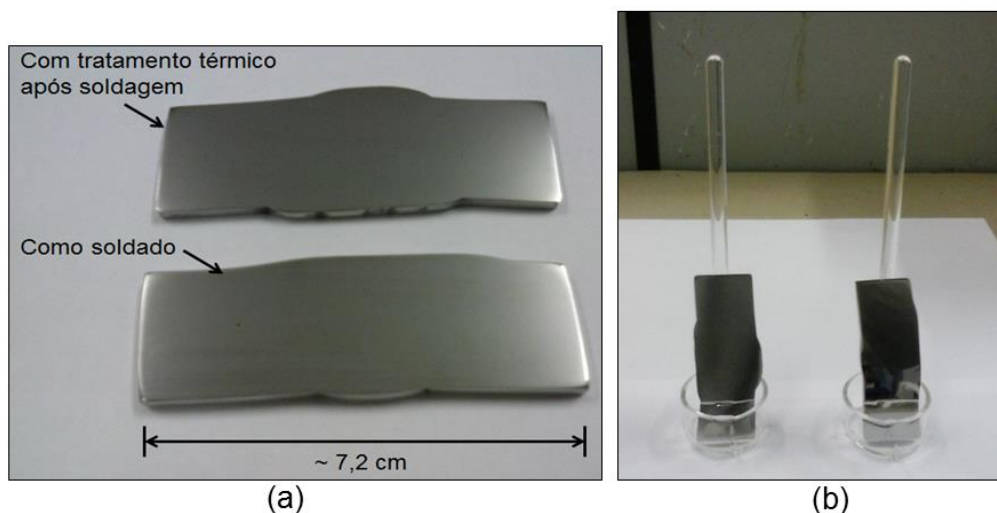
Ensaio de imersão: (a) corpos de prova e (b) suporte de vidro utilizado para imersão.
